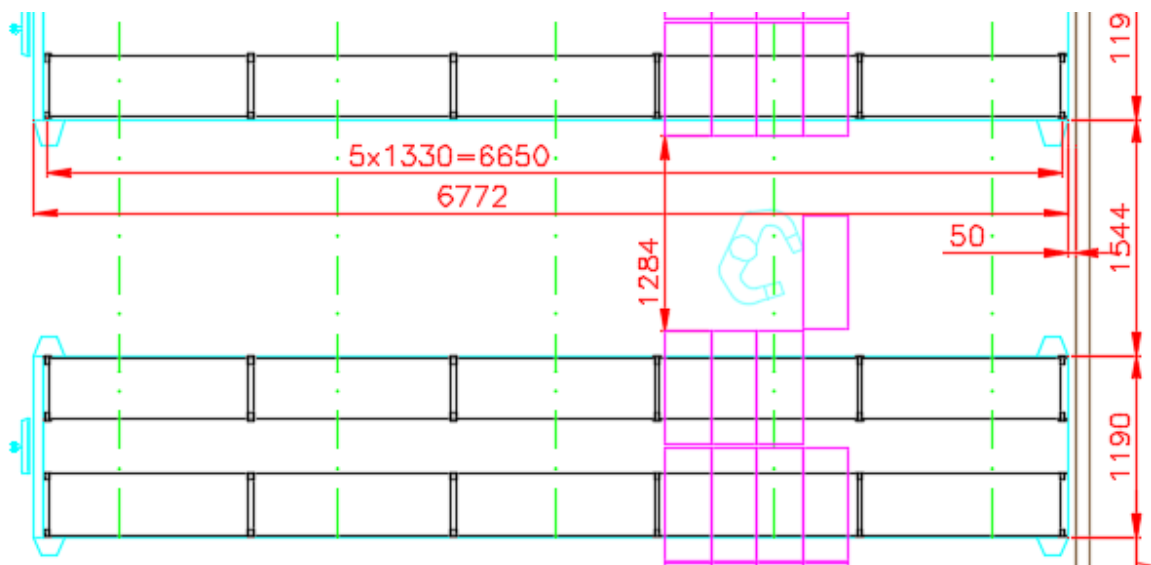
CAD výkres pro pojízdné regály v poli C [Autor]
